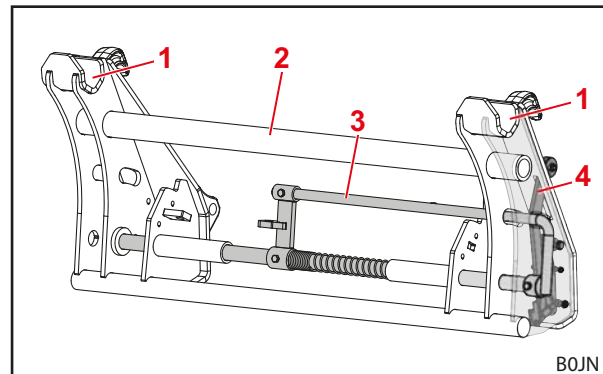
Aufbau MX-Werkzeugadapter – Vorderansicht
